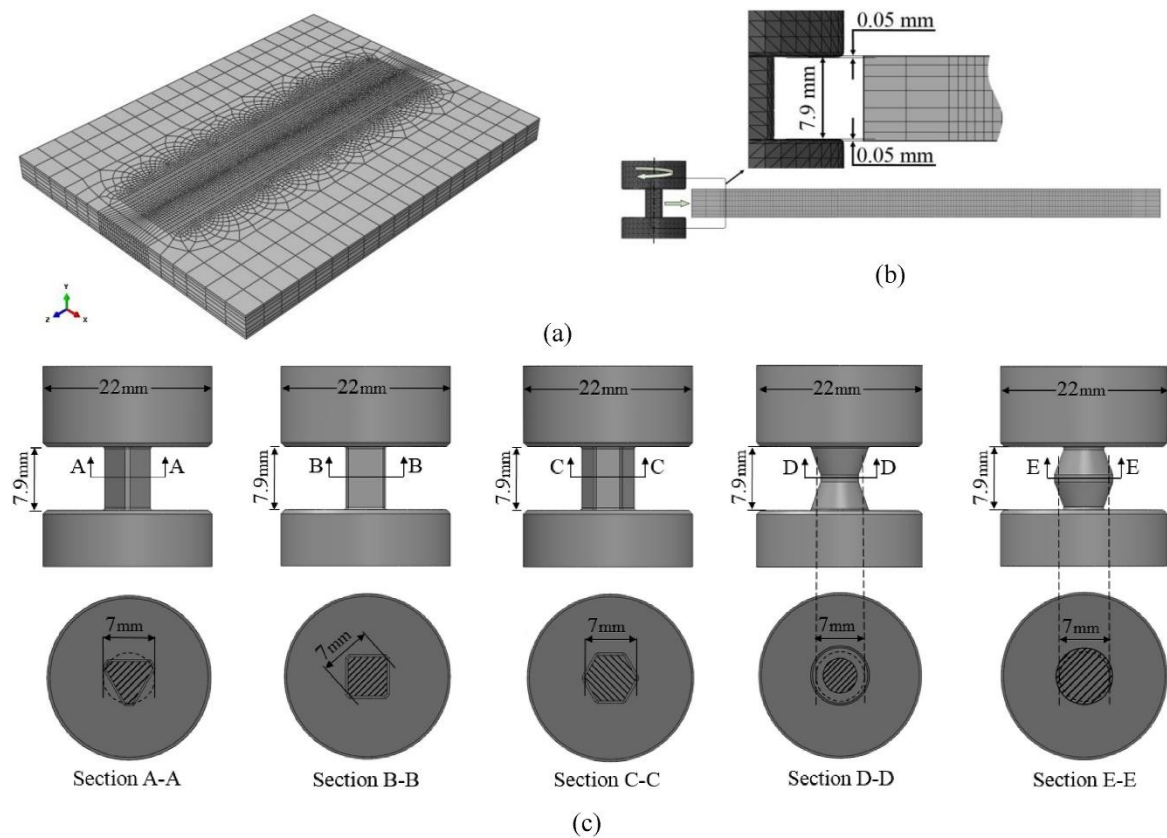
(a) Maillage des plaques de métal de base, (b) position de l'outil dans la direction de soudage contre les plaques en début de procédé et (c) géométries de l'outil et sections de pions modélisées pour la simulation du procédé de BT-FSW de plaques de magnésium [37]
